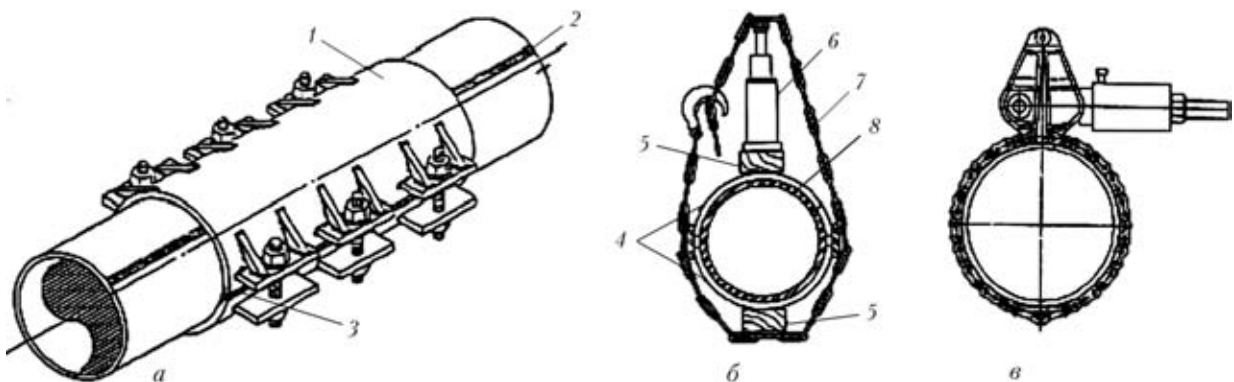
Схематическое изображение механических способов обеспечения прилегания муфты к стенке трубы [2]: *а* — болтовой; *б* — стандартный; *в* — с защемлением цепи; *1* — ремонтная муфта; *2* — продольный сварной шов; *3* — сварной шов с полным проплавлением и сплавлением с подложкой (наиболее употребимы два симметрично расположенных соединения); *4* — половины муфты с боковыми опорами; *5* — деревянная опорная рама; *6* — гидравлический пресс; *7* — высокопрочная цепь; *8* — ремонтируемый трубопровод
